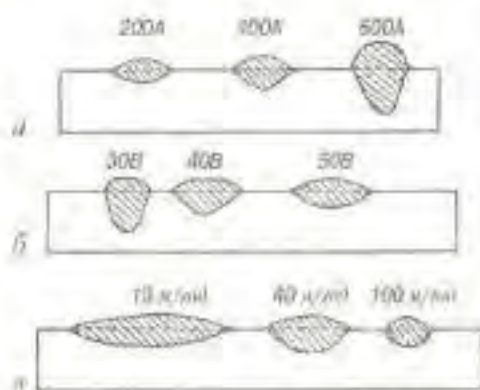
Вплив сили зварювального струму (а), напруги дуги (б) і швидкості зварювання (в) на геометричні розміри і форму шва
